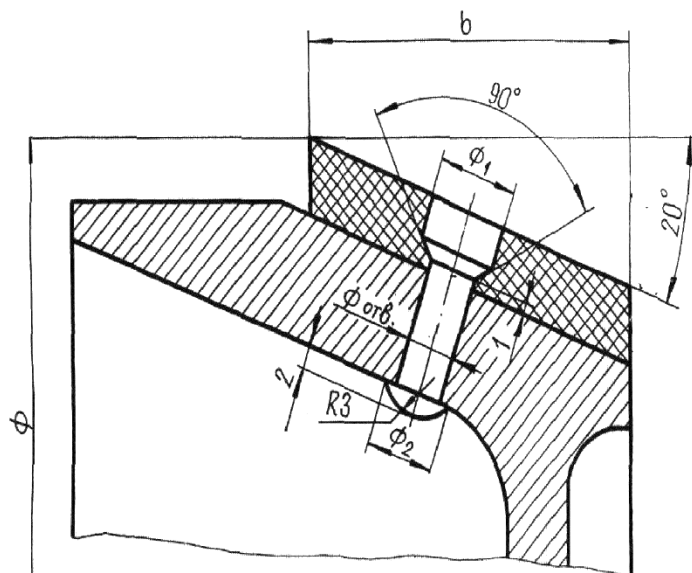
Первоначальный диаметр и угол поверхности тормозного диска электродвигателей подъемного механизма
